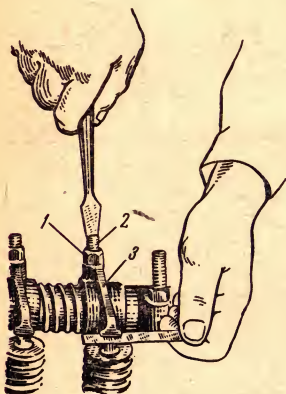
Регулировка зазоров клапанов двигателей Д-50Л, Д-65М и Д-65Н:
